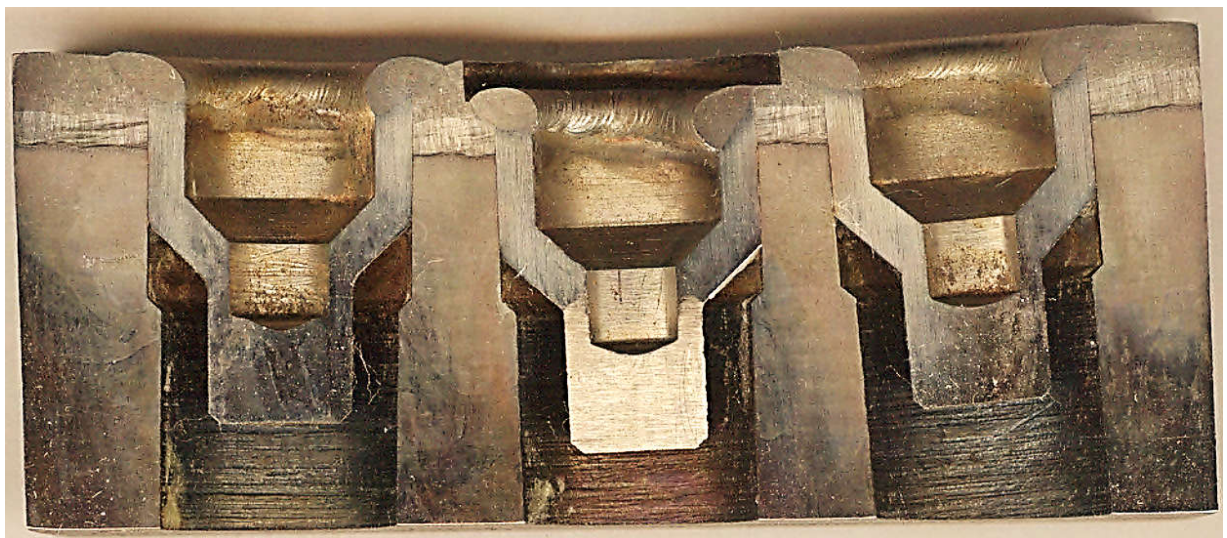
Макроструктура зварних з'єднань заглушок з трубною дошкою
